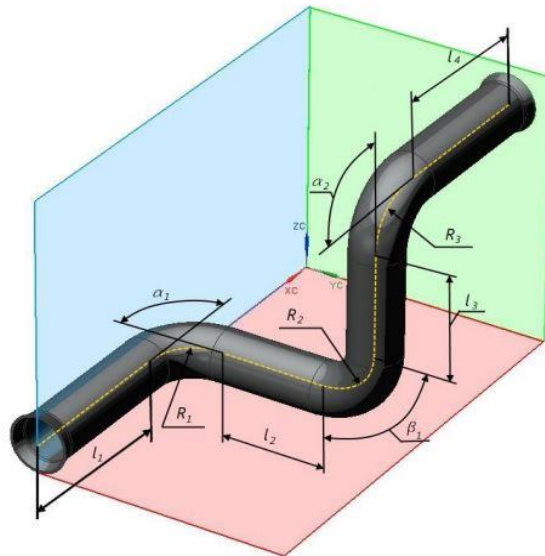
Патрубок круглого перерізу зігнутої форми з обробленими торцями:
